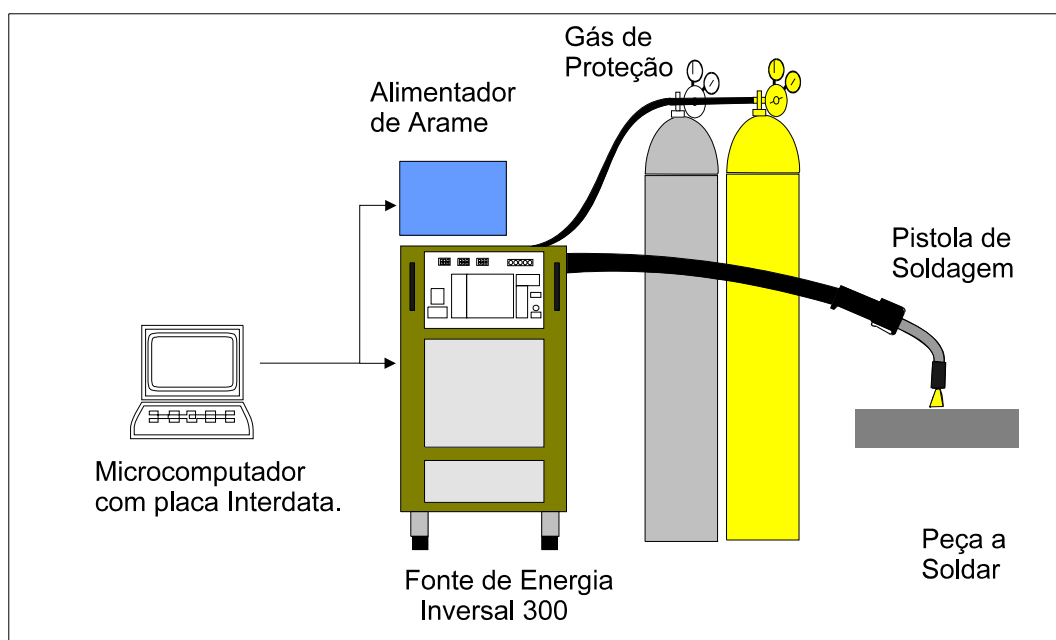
Equipamento usado para soldagem MIG/MAG
